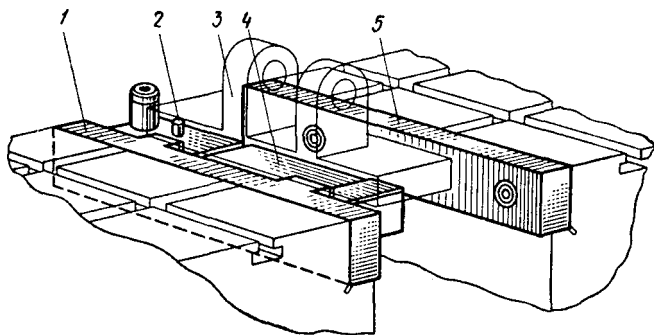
Наладка на универсально-наладочные тиски для крепления вилок при фрезеровании
